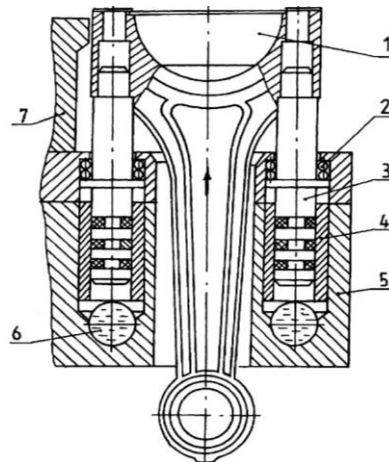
Пристосування з гідрозатискувачем для фрезерування площин роз'єму шатунів і кришок: 1 — сектор, 2 — пружина, 3 — плунжер, 4 — втулка, 5 — корпус, 6 — робоча рідина, 7 — направляюча
